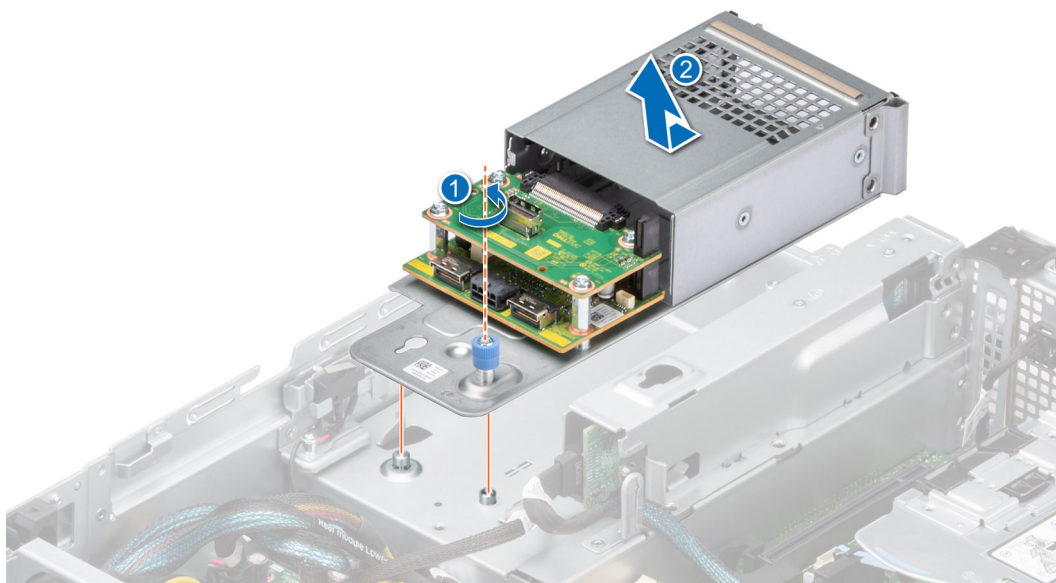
Entfernen des hinteren Laufwerksmoduls
